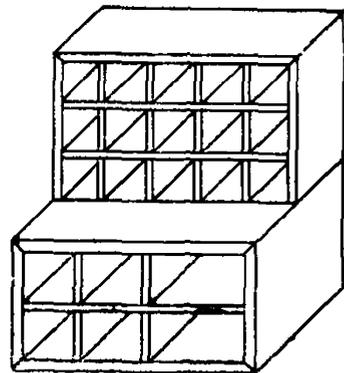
Стеллаж для хранения деталей и протирачного материала
